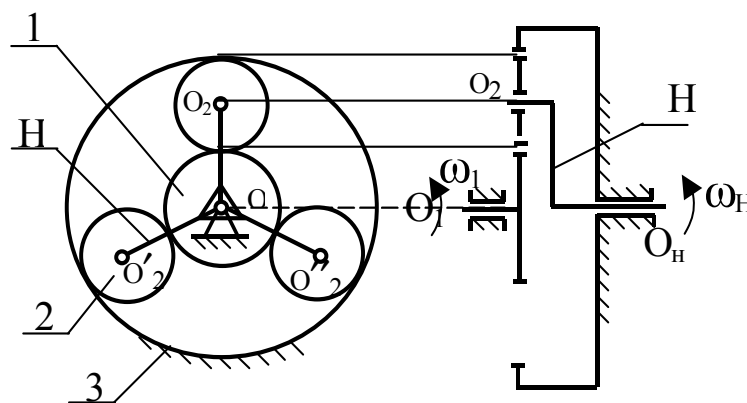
Схема планетарного механизма (редуктор Джемса)
